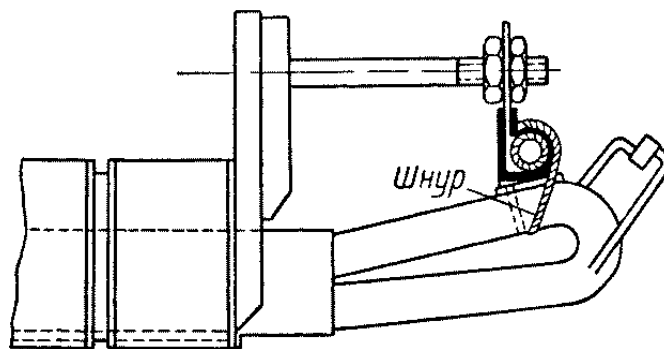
Крепление лобовых частей двухслойной обмотки.
